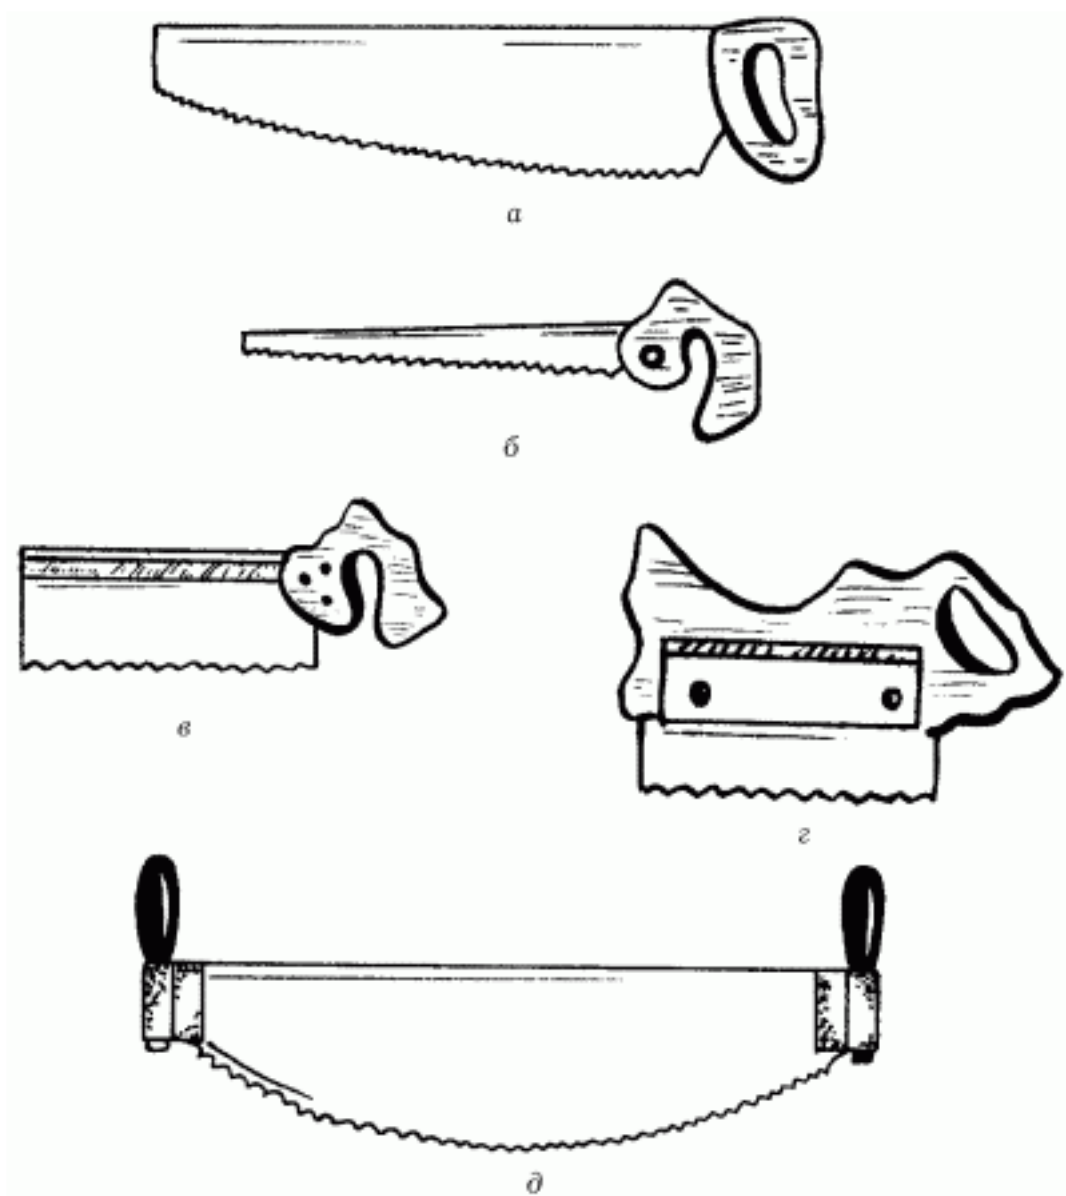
Виды ножовок: а – поперечная широкая; б – узкая; в – с обушком; г – ножовка-наградка; д – двуручная поперечная пила.
